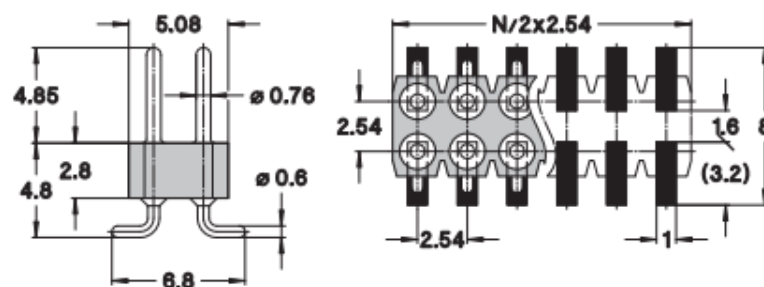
Huella del array de pines SMD (dimensiones en mm) [10].
